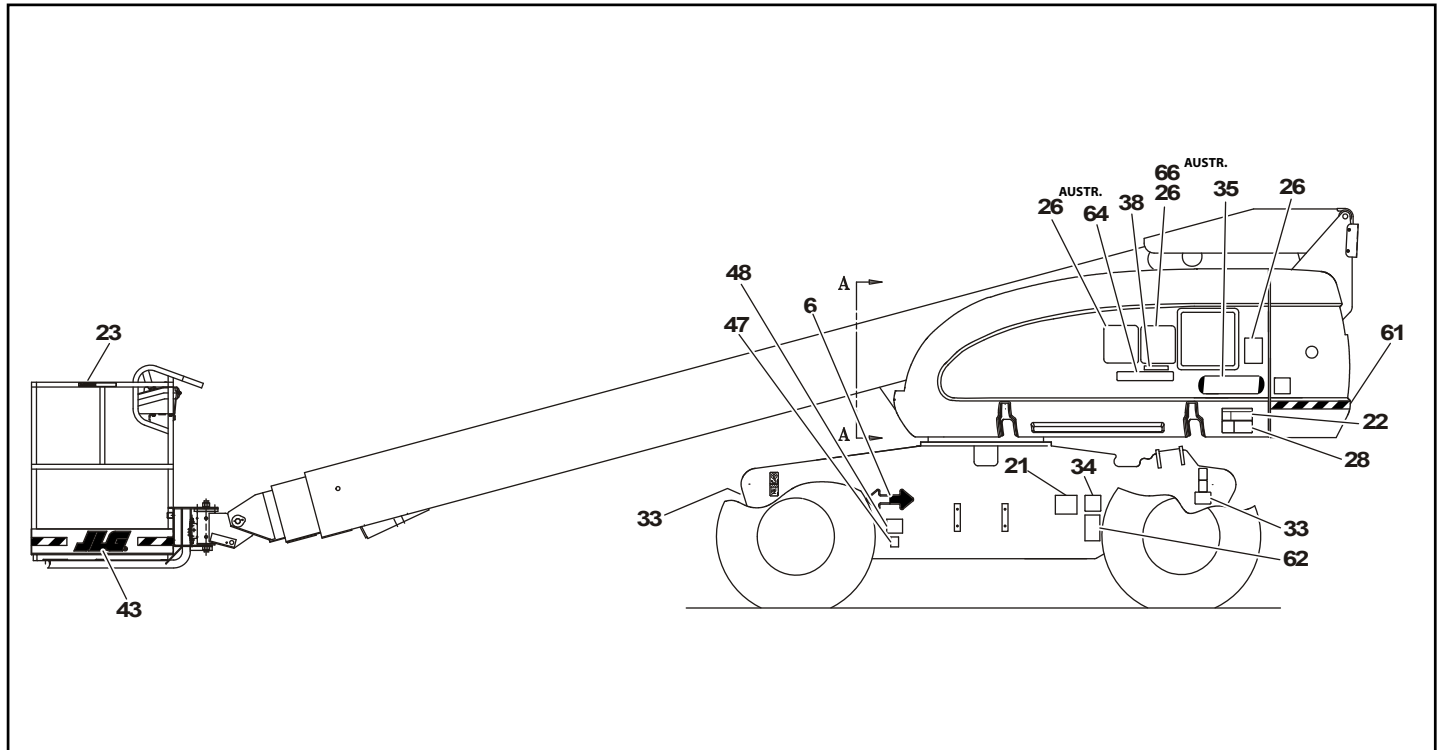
Placering av dekaler – Blad 2 av 4
